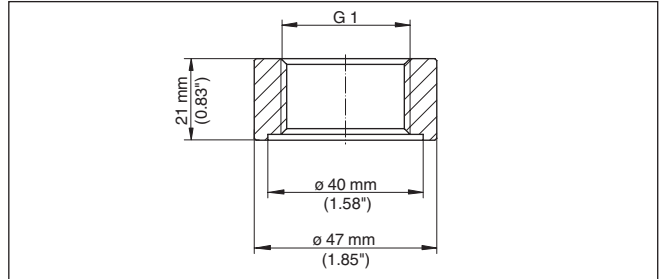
Maße Einschweißstutzen G1 (DIN 3852-X)
